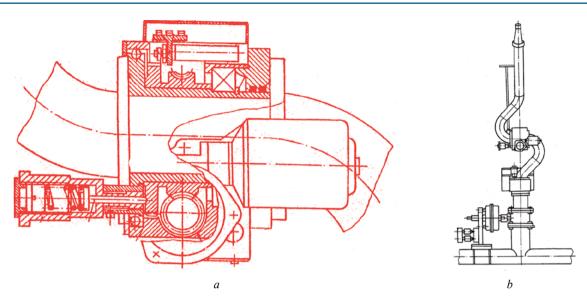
Механизм наведения (a) и общий вид пожарного монитора (b)
